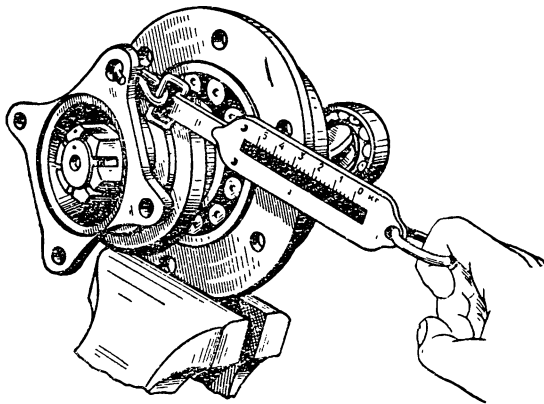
Проверка затяжки подшипников ведущей шестерни динамометром
